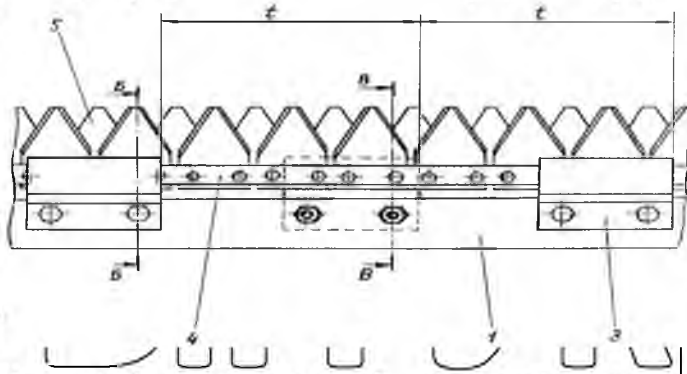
Безпальцевий ріжучий апарат з установленими нижніми і верхніми ножами: 1 - брус; 2 - нижні направляючі прижими; 3 - верхні прижими; 4 - спинка; 6 - сегменти.
